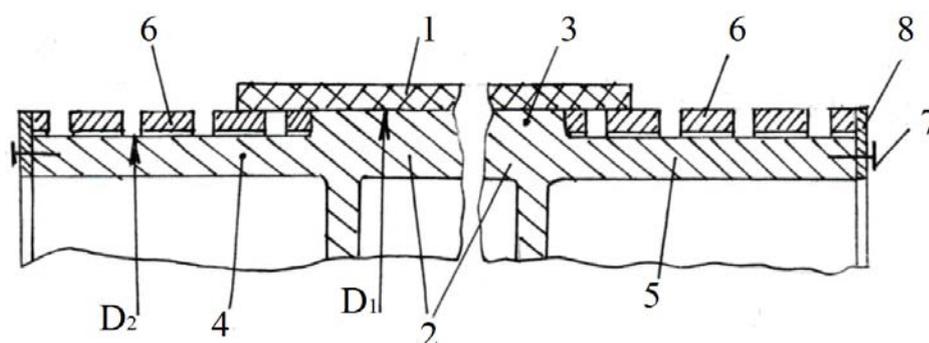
Приводной барабан ленточного конвейера [5]
